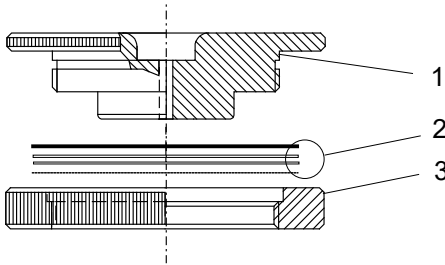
Matrize für Mitteldrucktiegel, Schnitt
